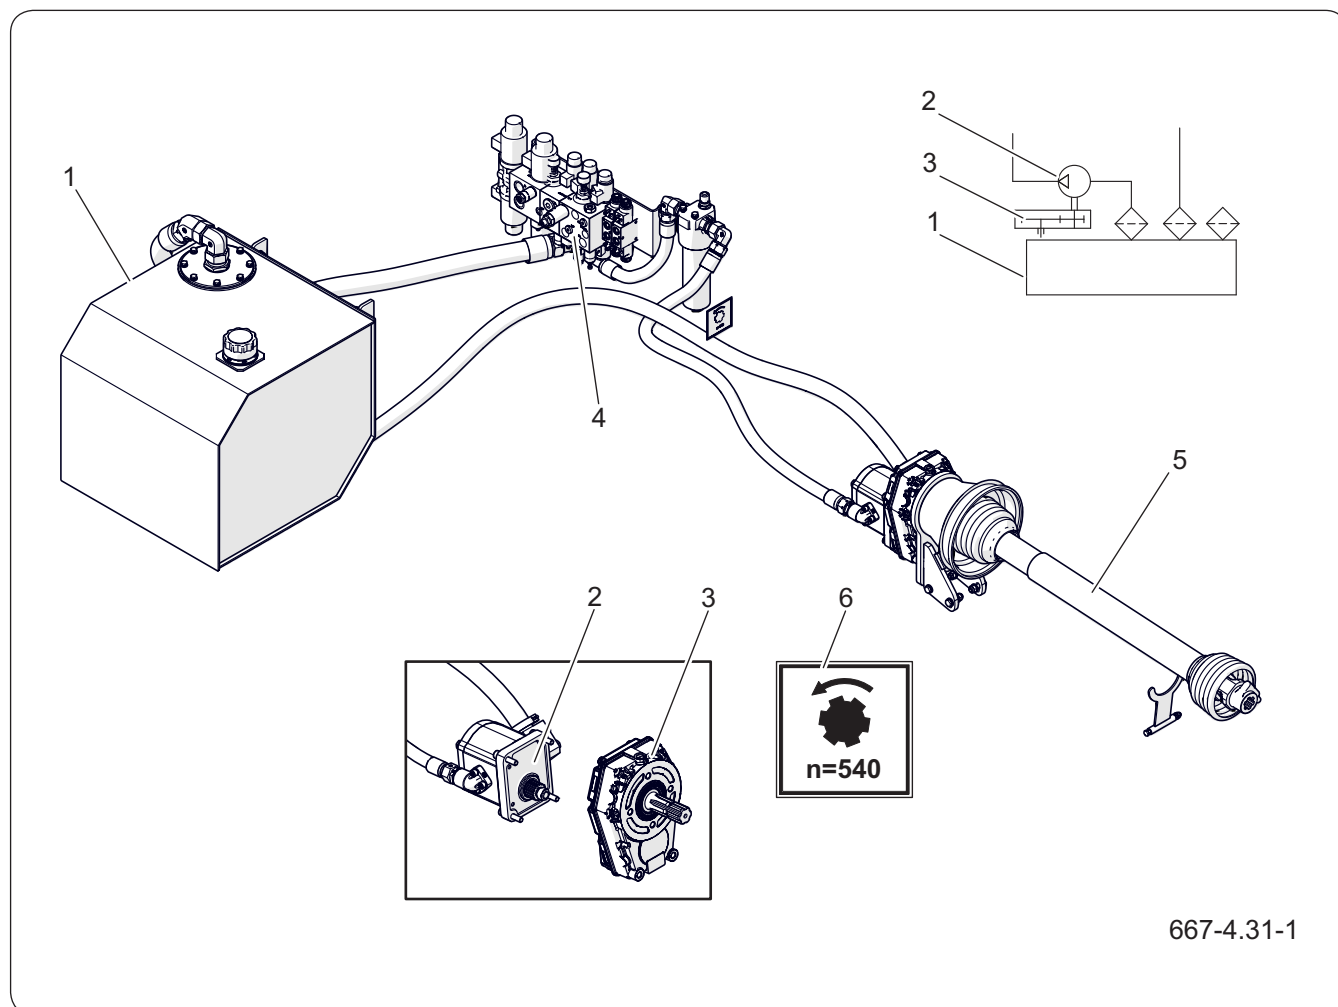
Konstrukce a schéma hydraulické soustavy s olejovou nádrží
